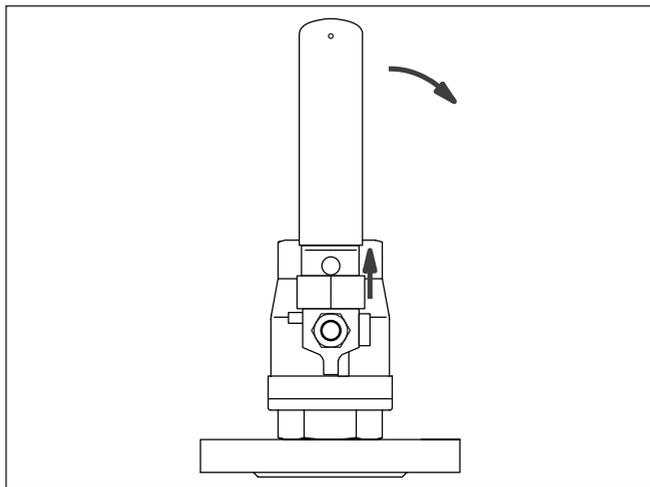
Maneggio del dispositivo di montaggio a valvola sferica
